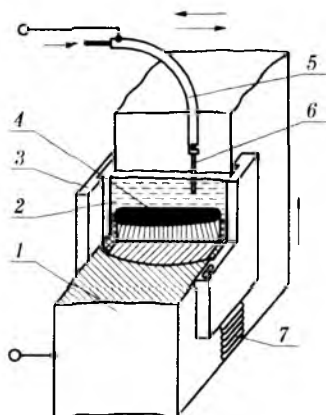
Схема электрошлаковой сварки:
